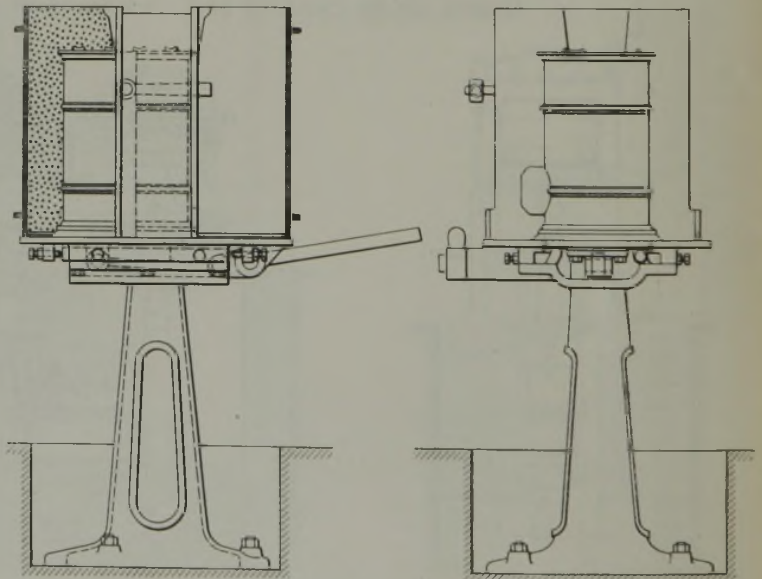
Durchzug-Formmaschine für den Mantel eines Quint-Ofens.
